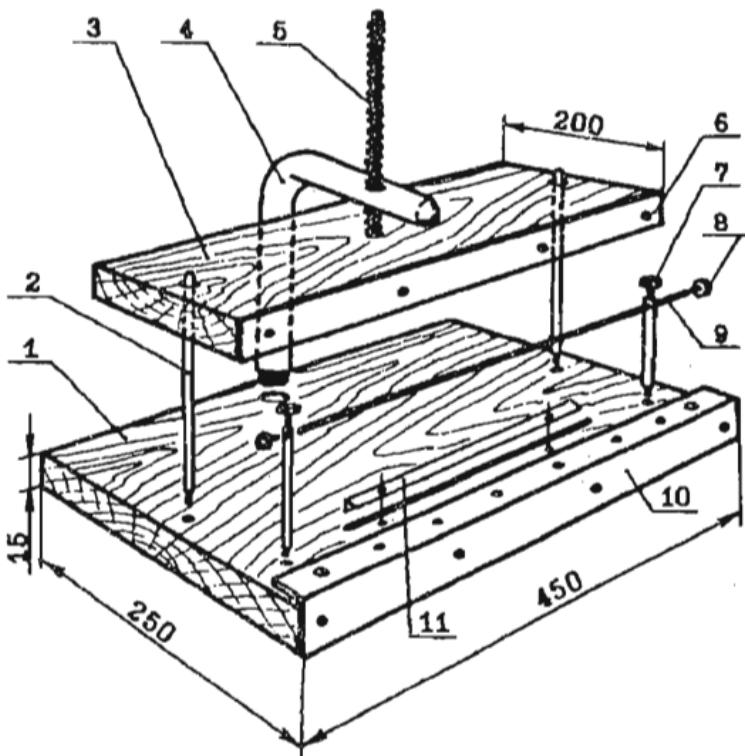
Универсальный переплетный станок; 1 - нижняя плита; 2 - направляющая стойка; 3 - верхняя (подвижная) плита; 4 - кронштейн; 5 - упорный винт; 6 - линейка для обрезки блока; 7 - зажимный винт; 8 - рукоятка; 9 - вал; 10 - уголок; 11 - фиксатор марли, тесьмы или шнурков
